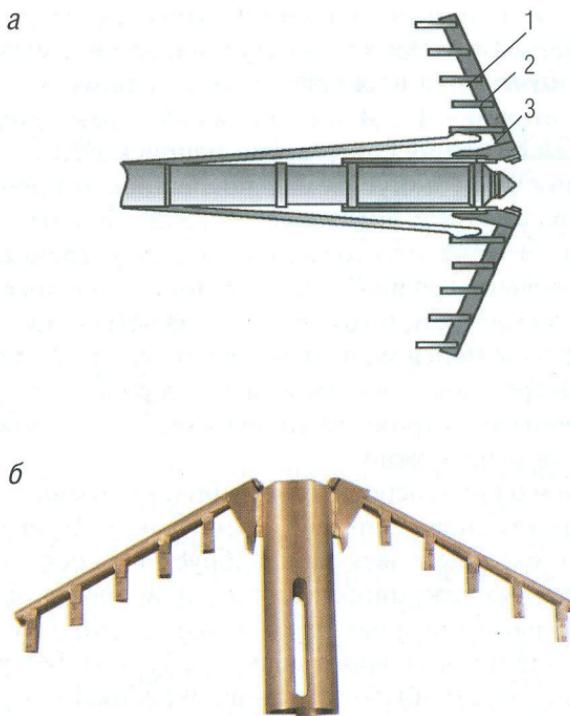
Калибровочное устройство типа «елочка» («гребенка»): а – схематическое изображение (1 – упоры, 2 – штанги, 3 – корпус); б – фотография
